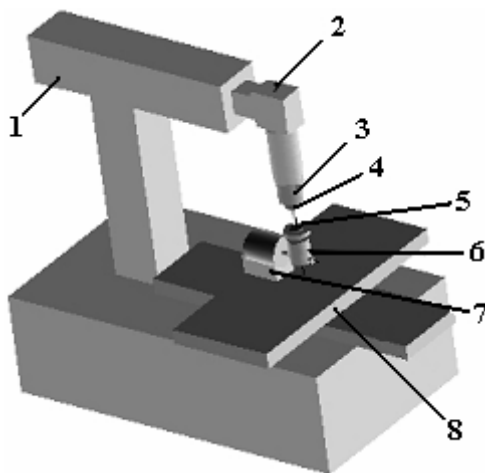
Схема экспериментального стенда: 1 – лазер; 2 – оптический блок; 3 – подвижная каретка; 4 – объектив; 5 – деталь; 6 – вращатель; 7 – поворотное приспособление; 8 – рабочий стол
